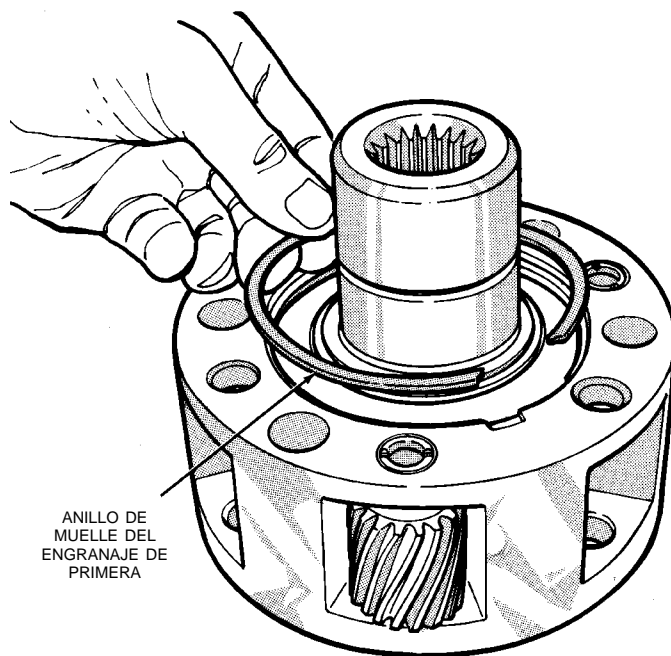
Desmontaje del conjunto de engranaje impulsor y de primera
